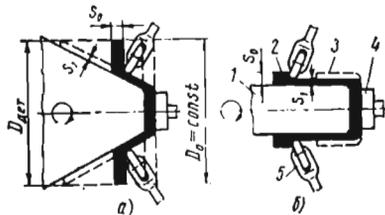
Оснастка для ротационной вытяжки с утонением из плоской (а) и цилиндрической (б) заготовки:
